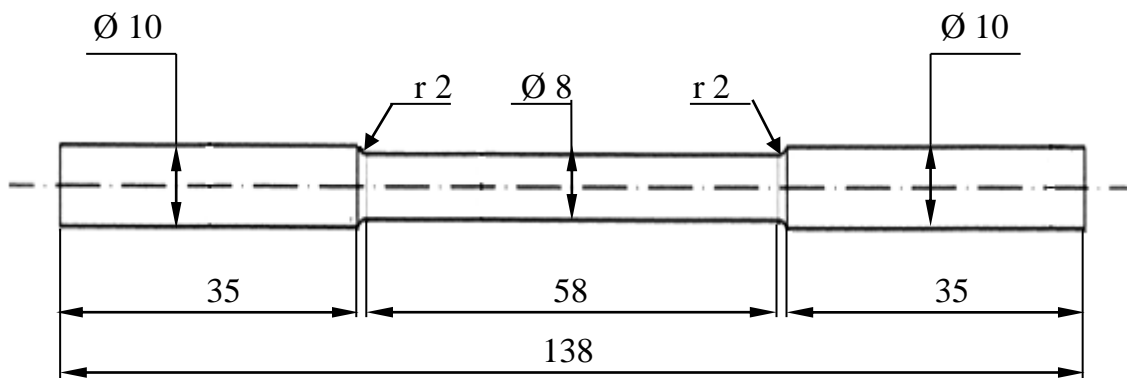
Eprouvette de soudage par friction avant découpage au centre.
